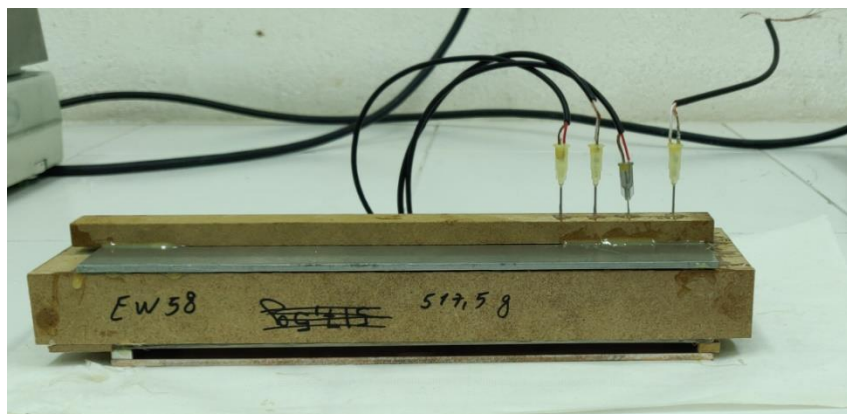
Montagem final para a soldadura EW58.
